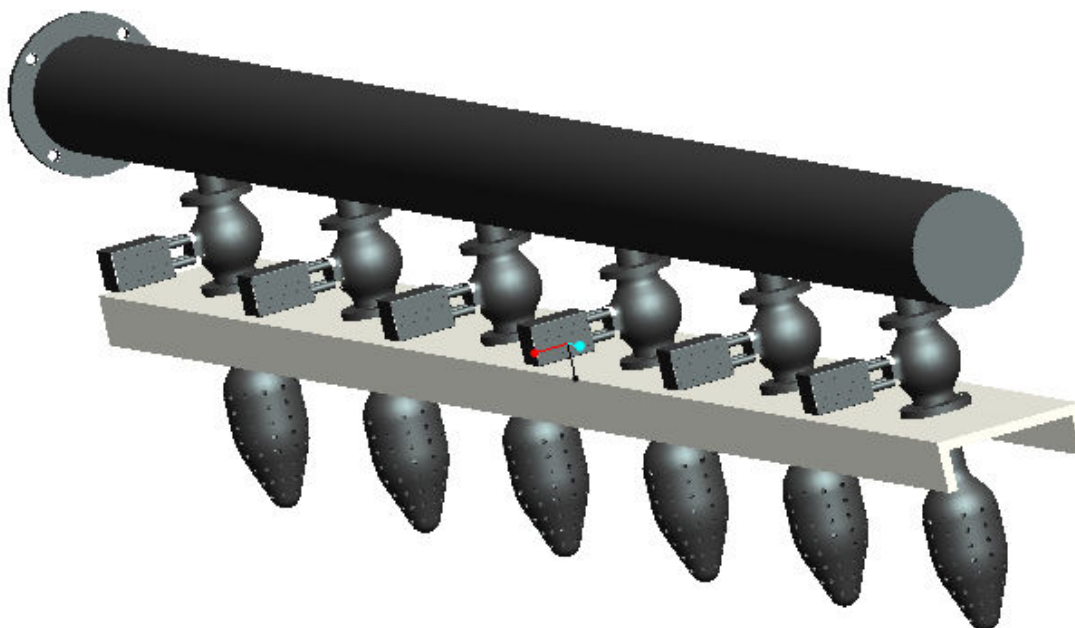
koncept parní skříně se speciální stříčkou
